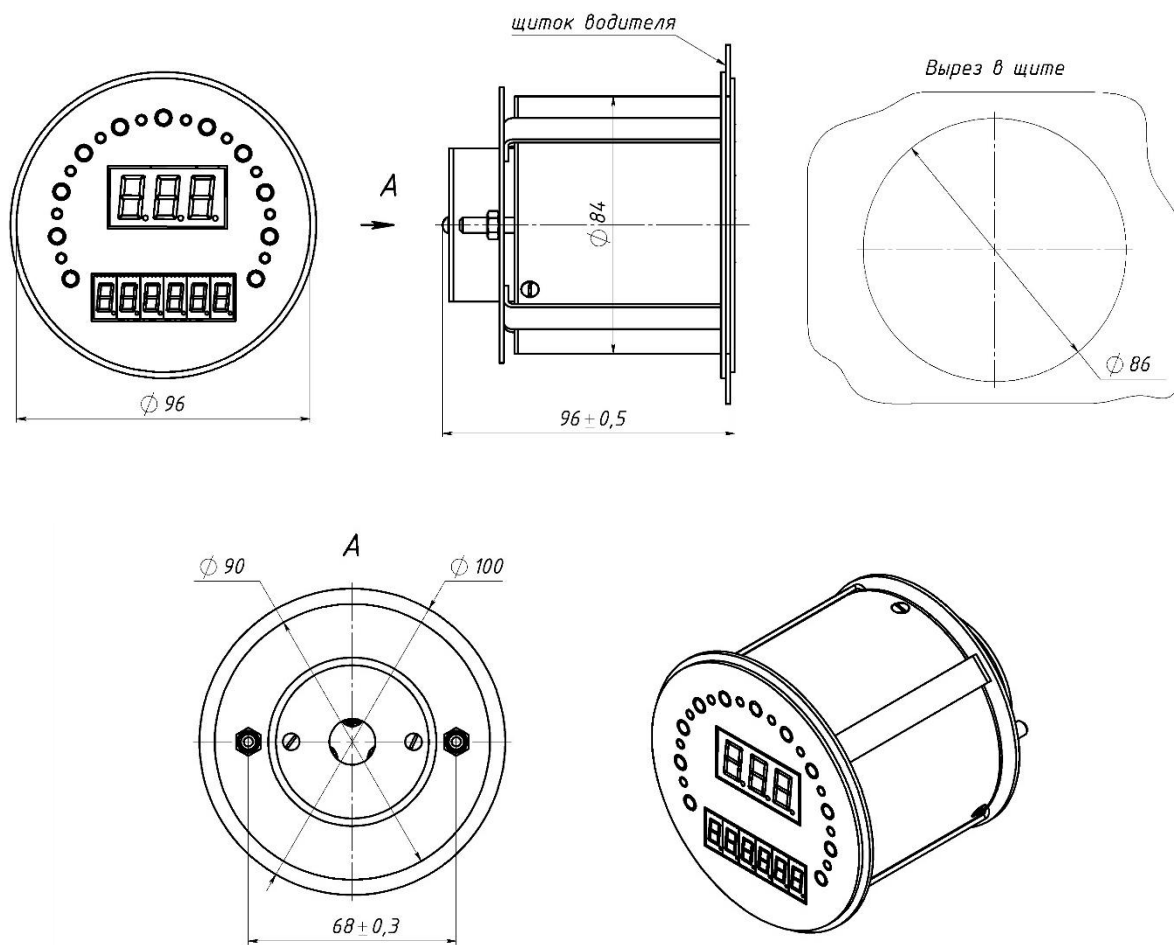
Габаритные и присоединительные размеры СПЦ
